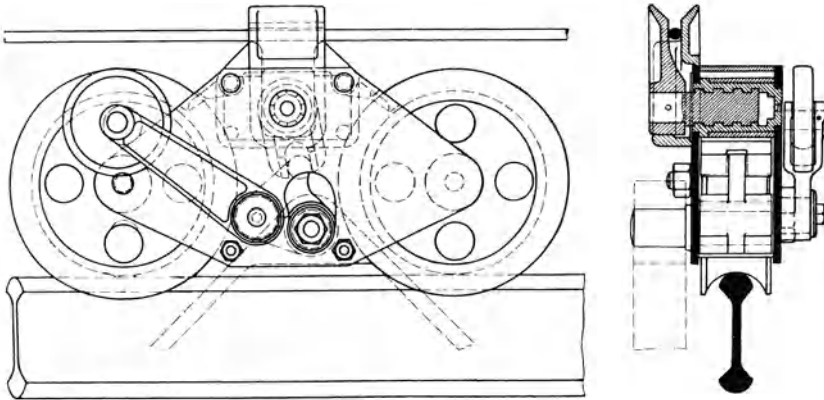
Gewichtskuppelapparat der Benrather Maschinenfabrik A.-G.
